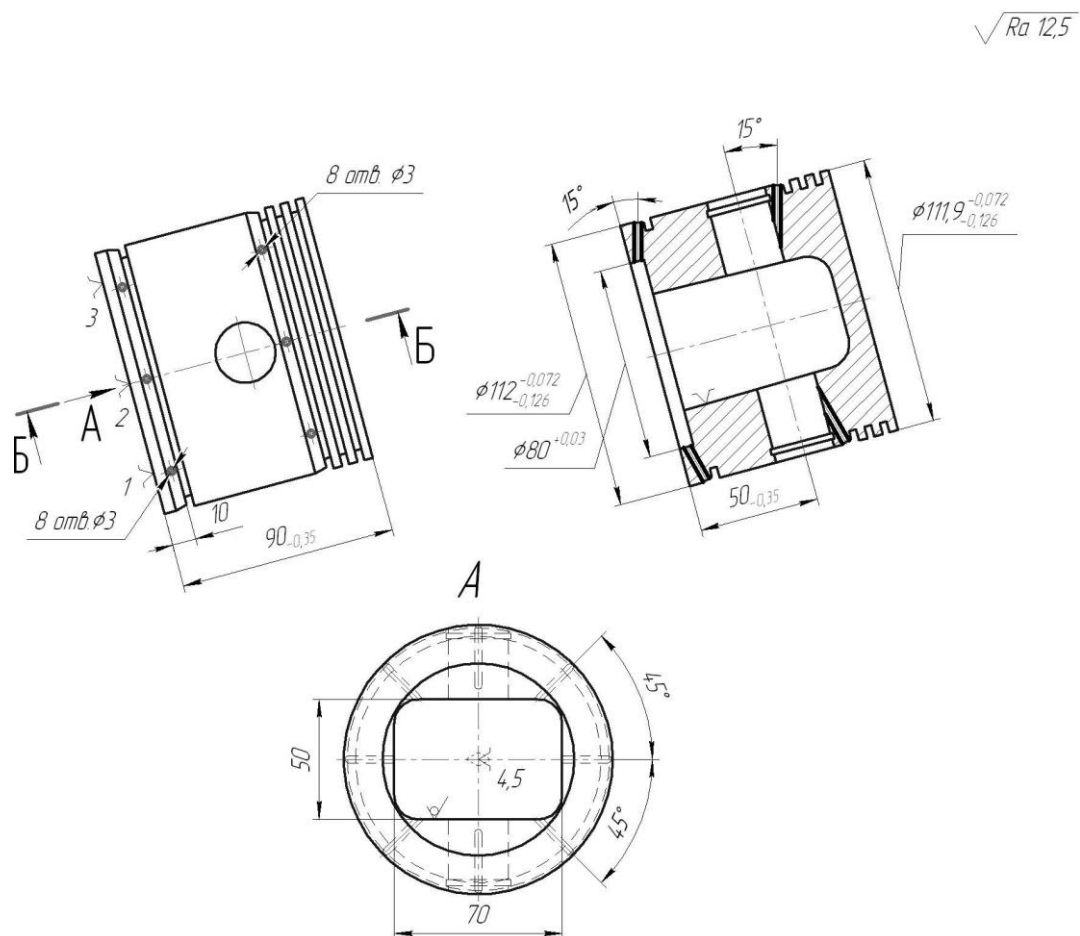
Схема базування оброблюваної деталі поршень компресора
